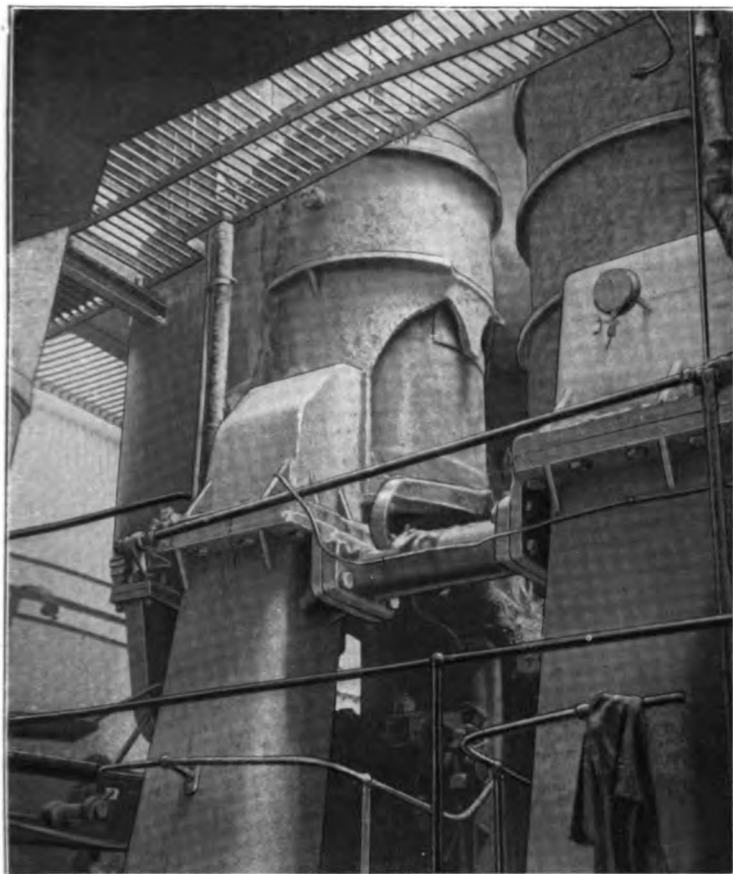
Dampfer »Kandelfels«, gesprengter Mitteldruckzylinder
